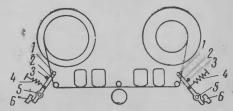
Конструкция автоматического устройства, управляющего направлением движения магнитной ленты.
